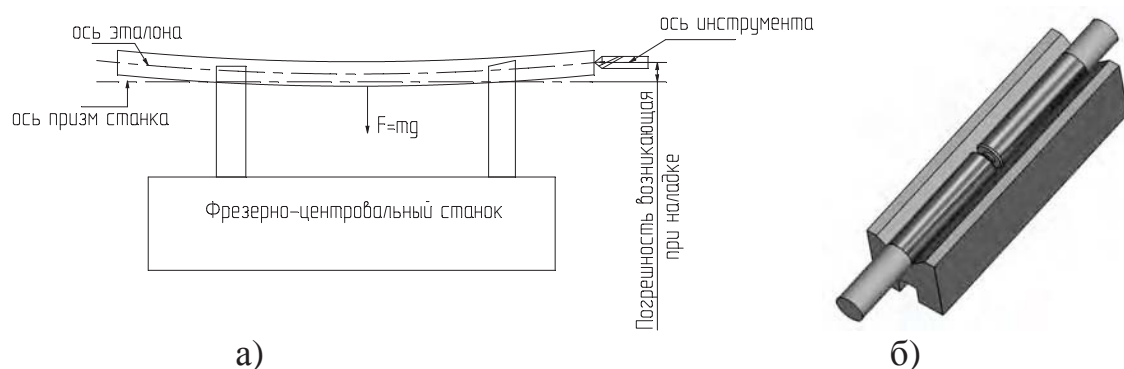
Существующая схема наладки фрезерно-центровального станка с помощью «эталонного» вала (а) и предлагаемый комплекс для наладки станков при изготовлении длинномерных деталей (б)
